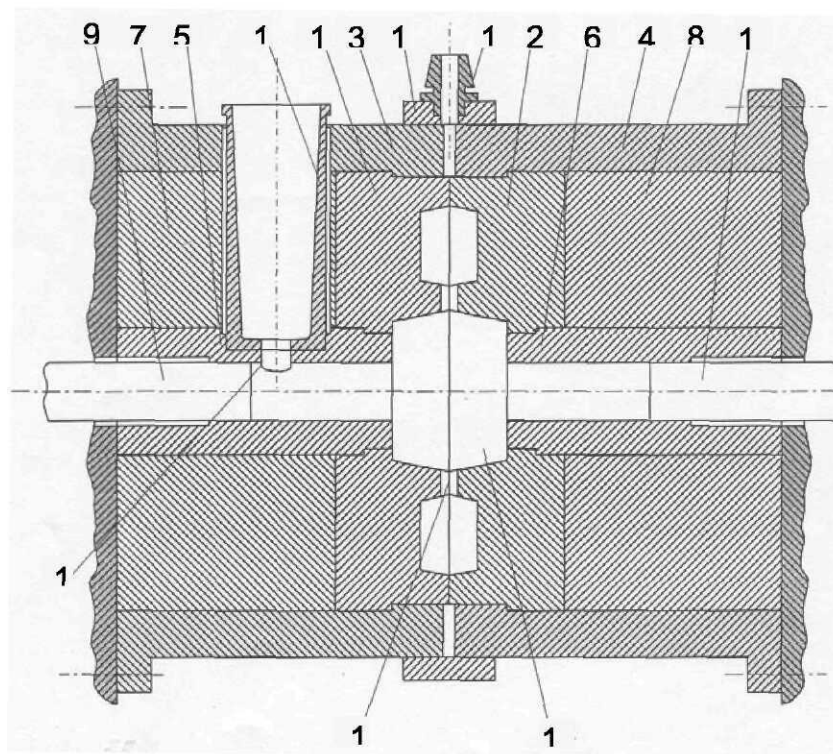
Схема процесса литья с вакуумированием и опрессовкой кристаллизующегося металла
